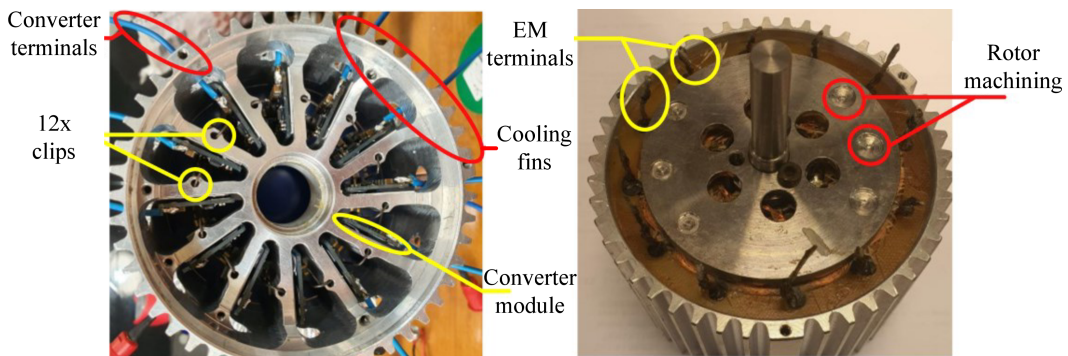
Vista frontale del dimostratore assemblato prima e dopo il montaggio della macchina elettrica.
